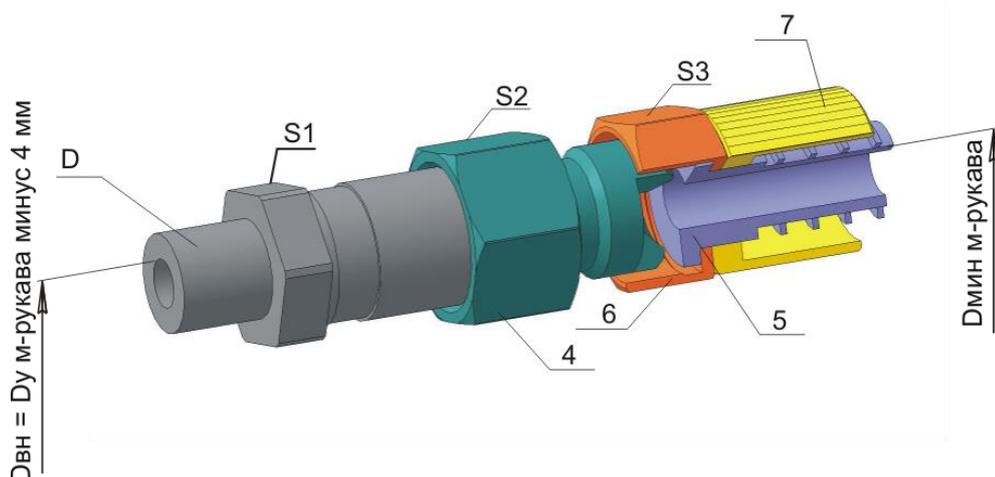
Конструкция кабельного ввода для монтажа кабеля в металлорукаве с ПВХ оболочкой
